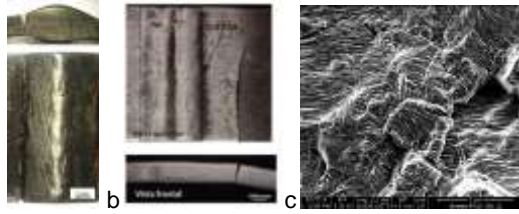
Ubicación de la fractura en las uniones soldadas: a-GMAW y b-PAW; c- Superficie de fractura probeta PAW.
